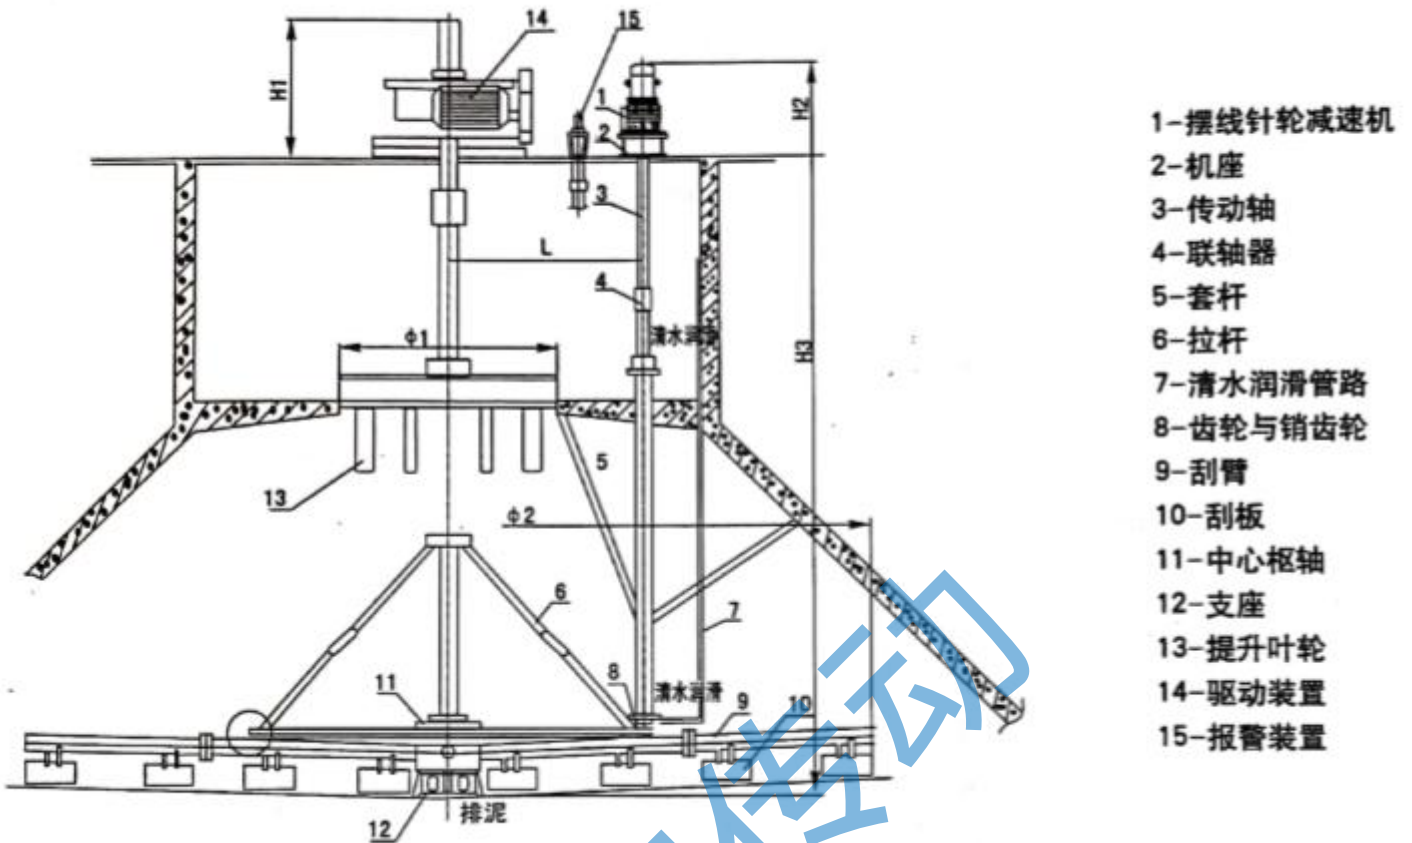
800 - 1800M³/h齿轮销齿轮传动刮泥机
